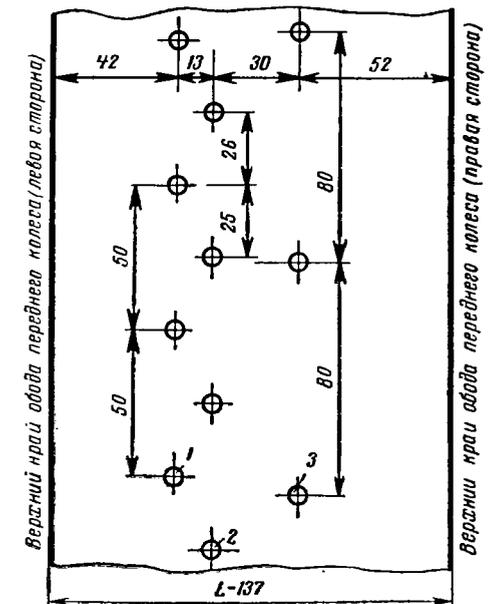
Расположение шипов на шине переднего колеса; 1 — первый ряд с левой стороны колеса; 2 — второй ряд; 3 — третий ряд шипов.
